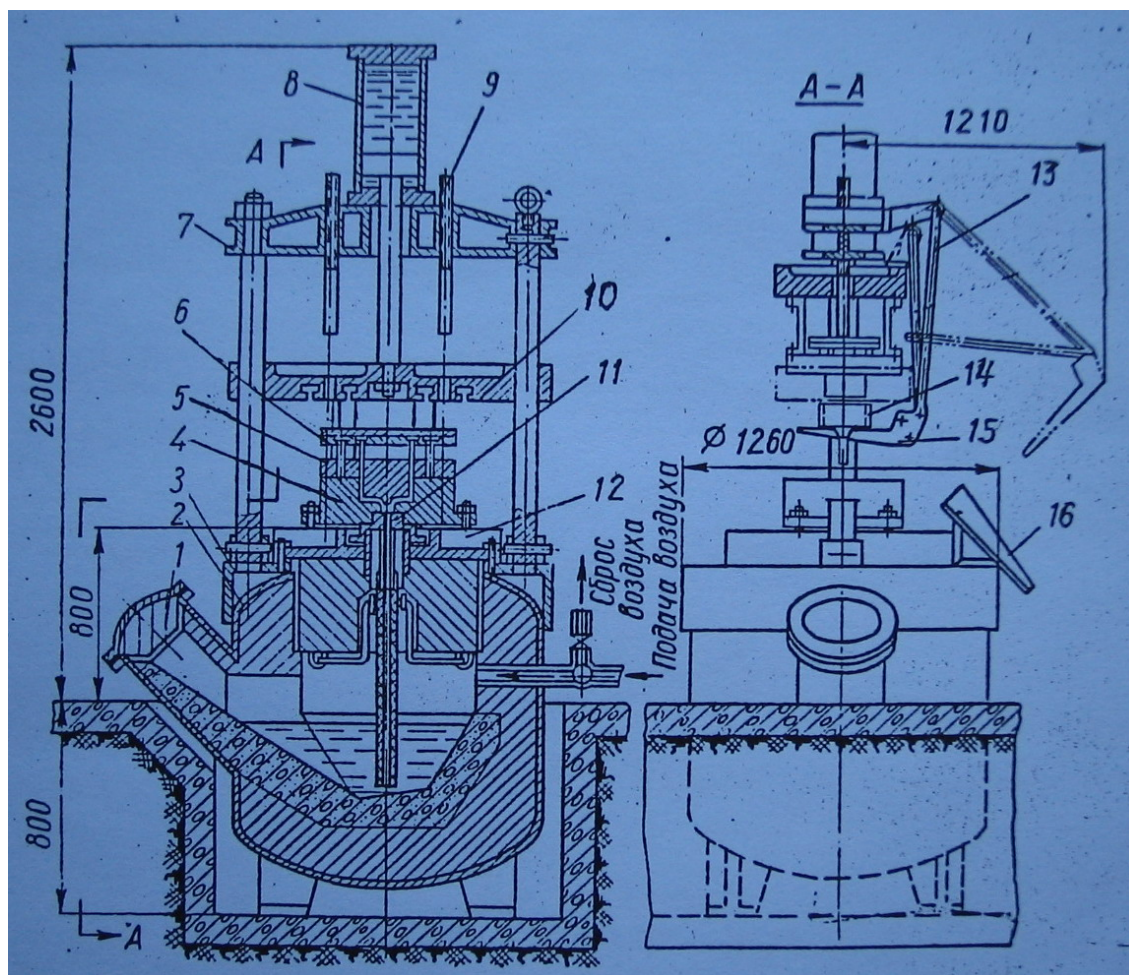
Установка ЛНД для получения отливок из алюминиевых сплавов.
